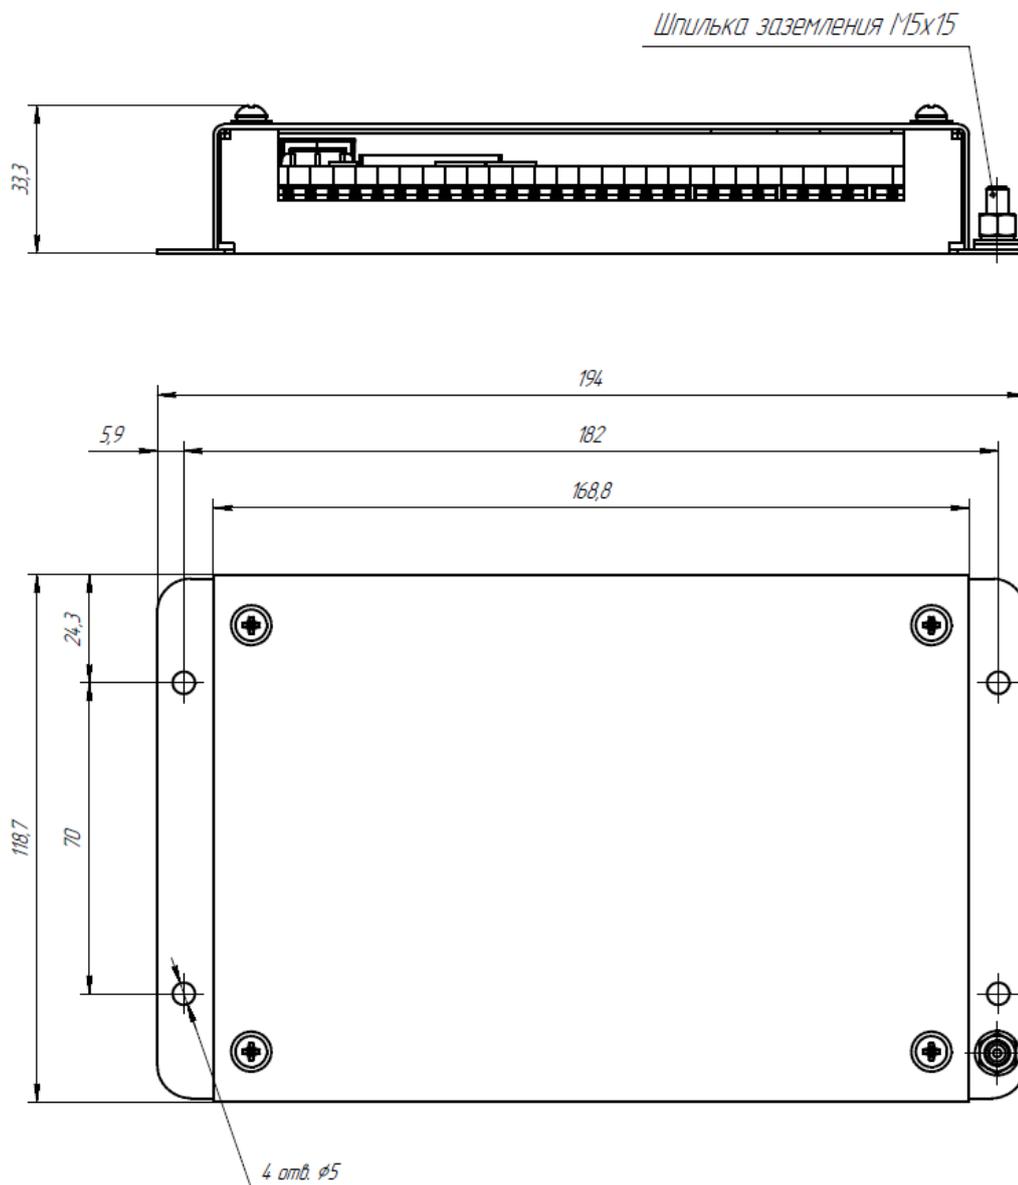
Габаритные и установочные размеры МДУ-102
